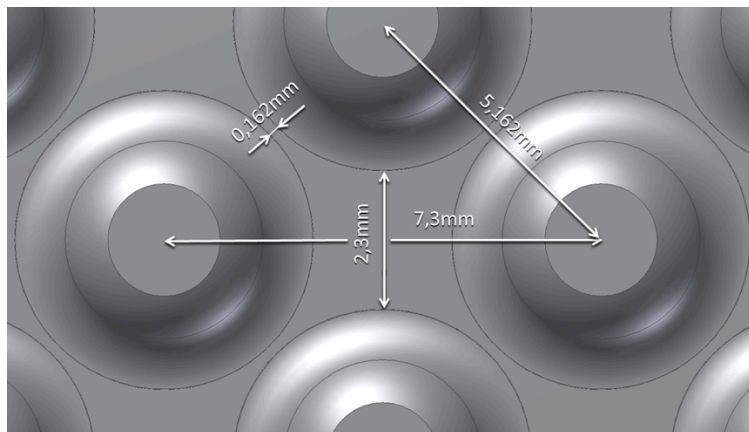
Detailansicht der Noppenstruktur mit eingezeichneten Noppenabständen
